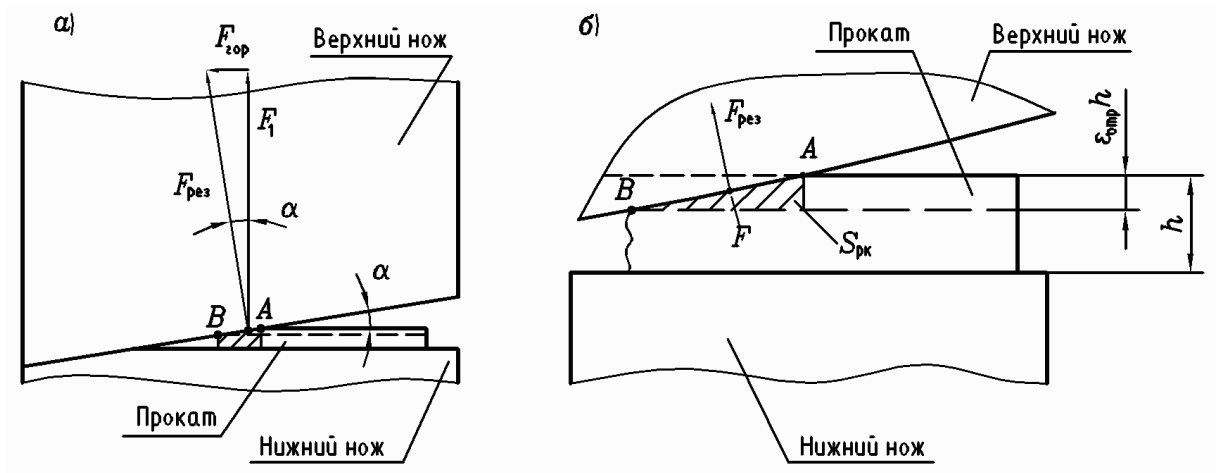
Угол реза α гильотинных ножниц; *б* ножниц с катящимся резом. *A* — точка врезания; *B* — точка отрыва металла.
